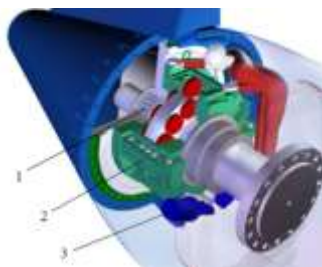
Схема упорного підшипника установок "Azipod XO":
